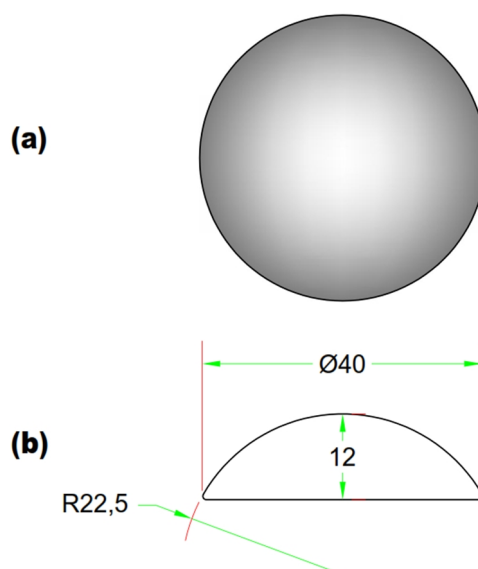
Diseño de colada (a) Vista superior (b) Vista frontal
